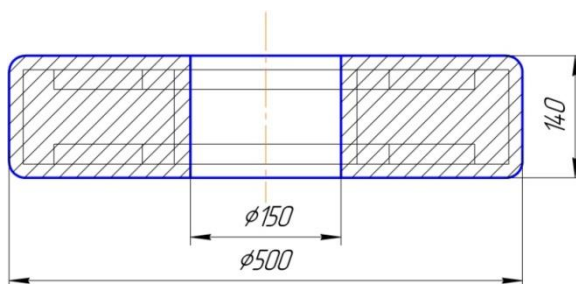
Поковка шестерни с прошитым отверстием
